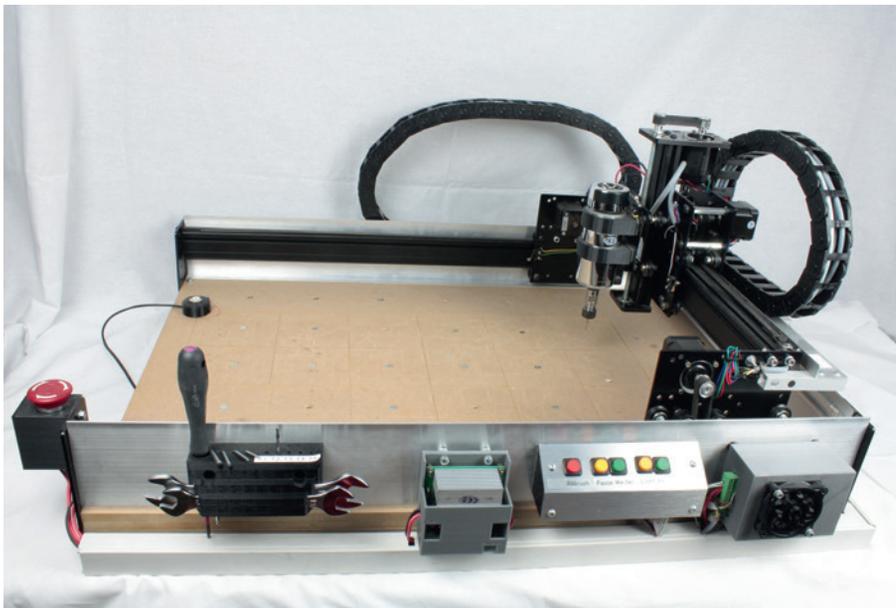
Im Buch bauen wir eine Shapeoko-Fräse.
